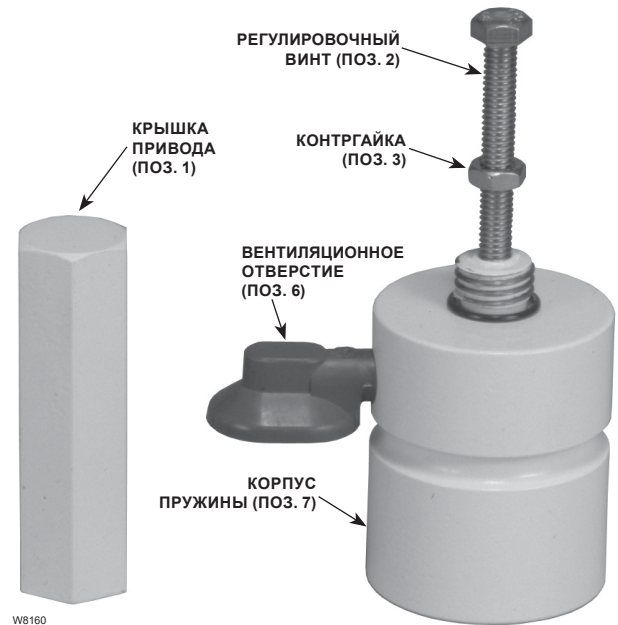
Корпус пружины, регулировочный винт и крышка привода
